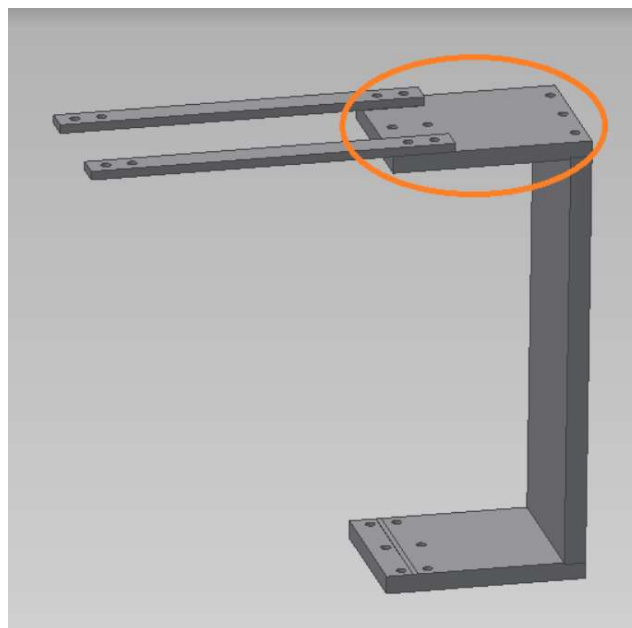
Detalle de los refuerzos longitudinales de unión.
